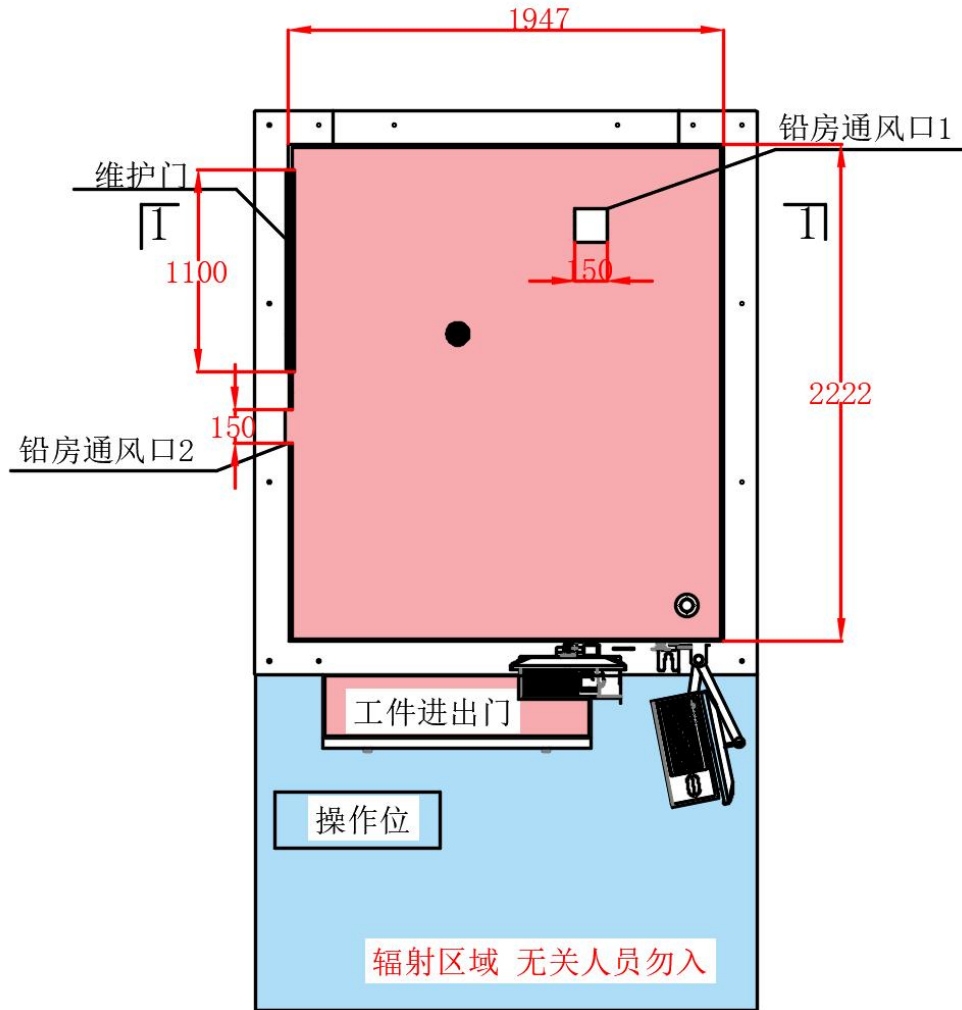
(a) L2161 型工业 CT 机辐射屏蔽室平面布置示意图 (mm)
